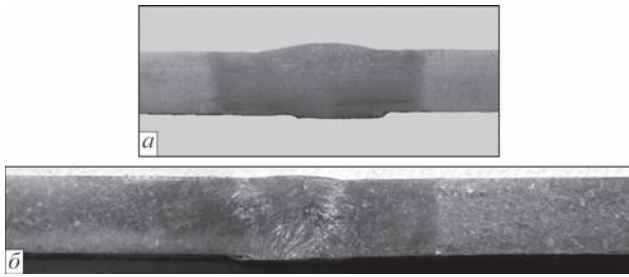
Поперечний макрошліф зварного з'єднання жароміцного титанового сплаву $Ti-6,5Al-5,3Zr-2,2Sn-0,6Mo-0,5Nb-0,75Si$, виконаного: *a* – ТІГ зварюванням; *б* – А-ТІГ зварюванням
